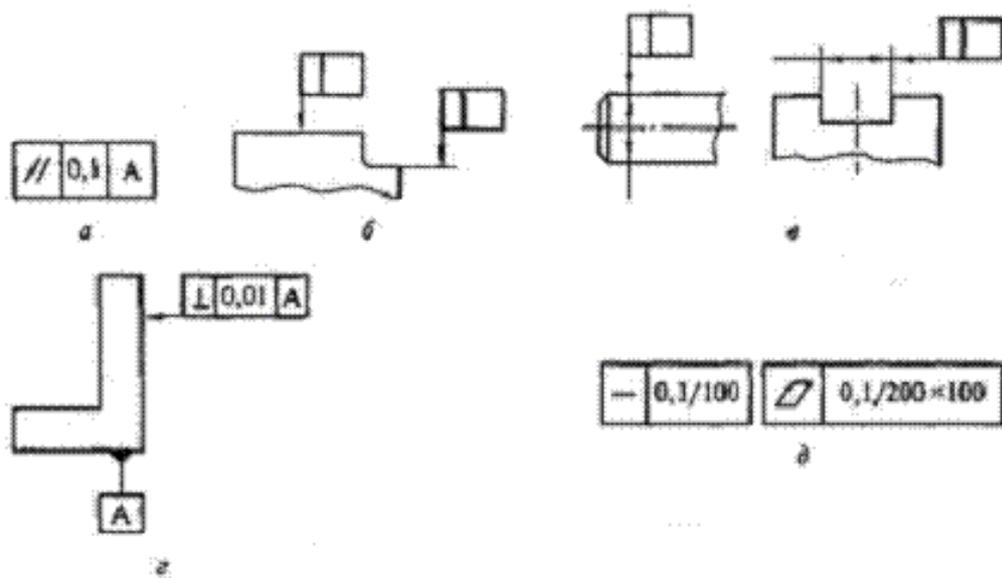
Условные обозначения допусков расположения и формы на чертежах
